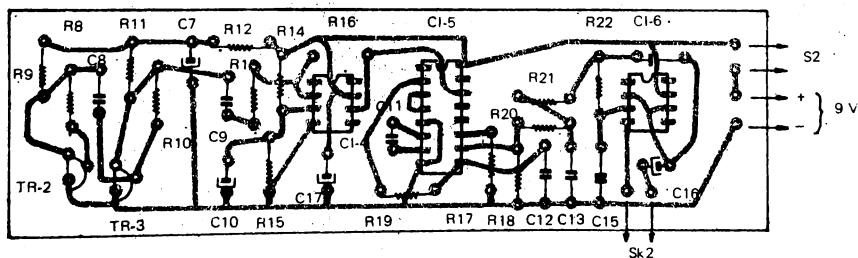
Disposición de componentes sobre el impreso del receptor.
